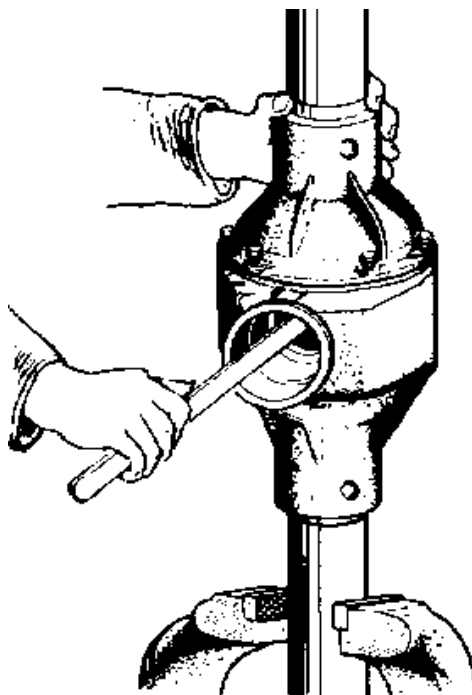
Напресування роликів підшипників диференціала, щоб замінити шестерні головної передачі разом з підшипниками диференціала
